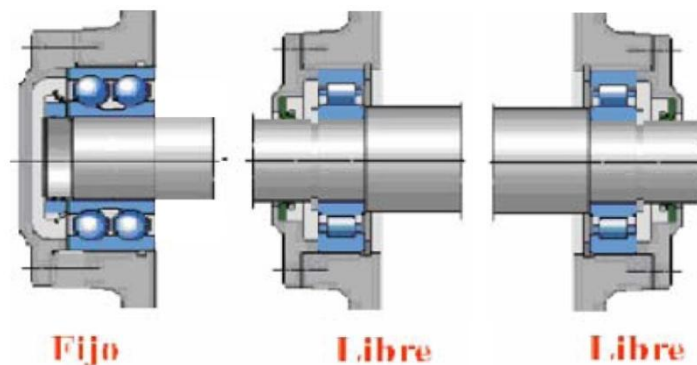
Disposición de rodamientos de rodillo y contacto angular en el eje principal.
